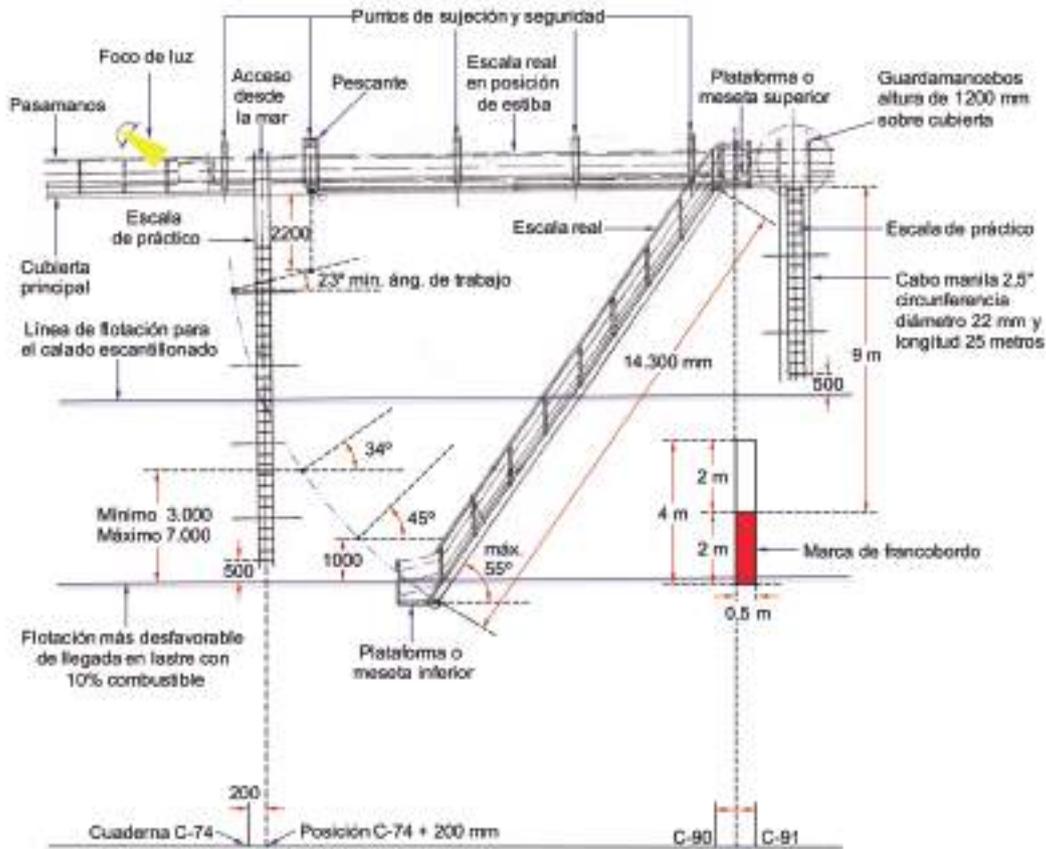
Disposición o escala combinada (práctico y real). Calado escantillonado⁵³.
